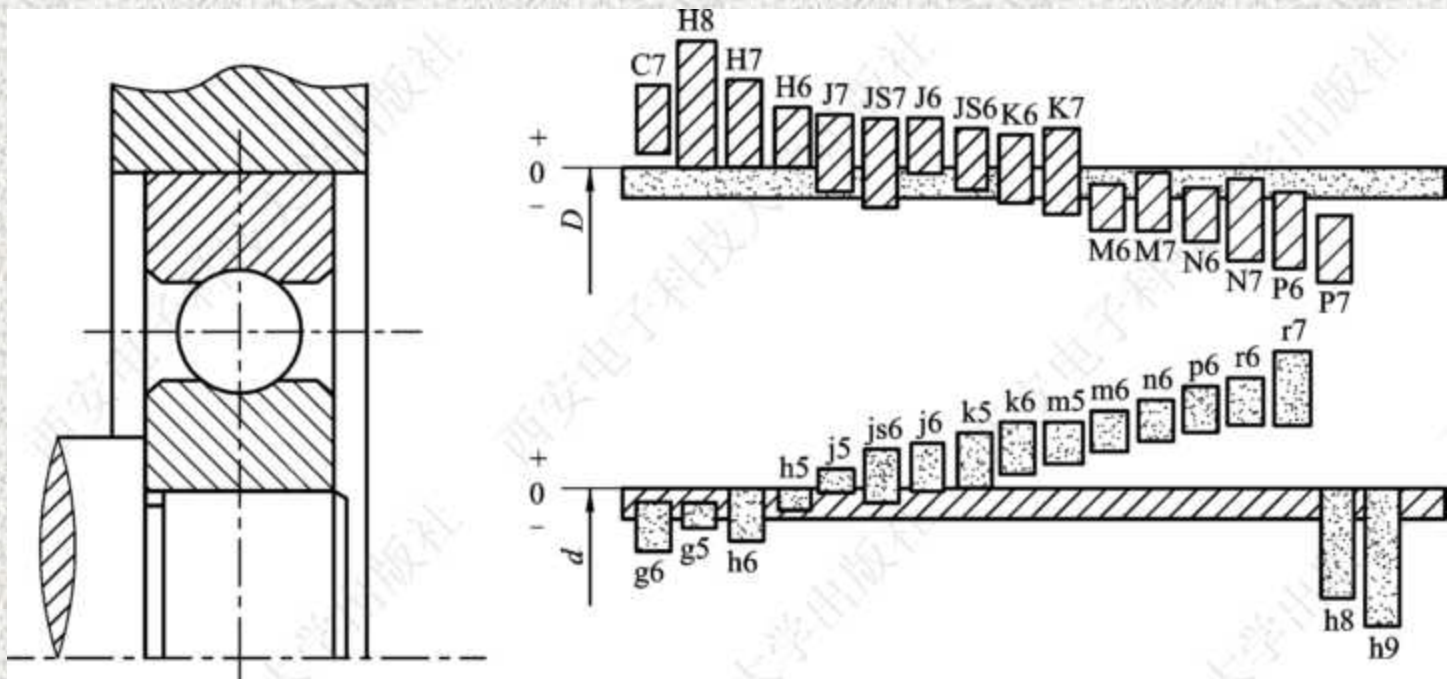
轴承与轴颈、外壳孔配合的公差带
